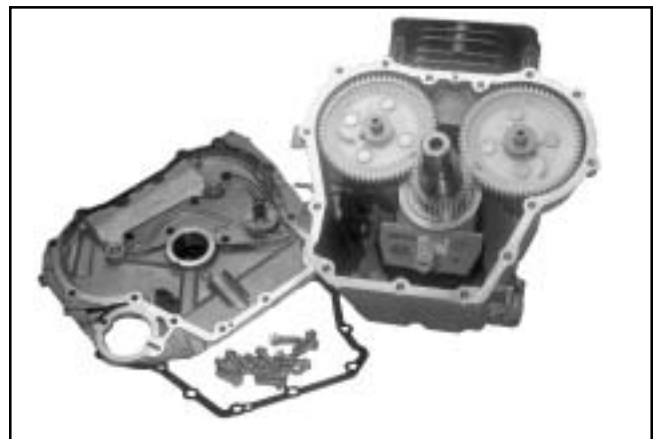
Placa de cierre y junta desmontadas del cárter.
